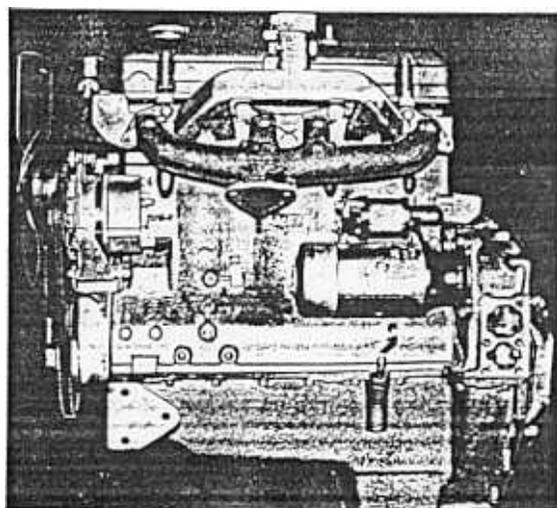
A-01-03 - Vista del lado izquierdo del motor EBR0
